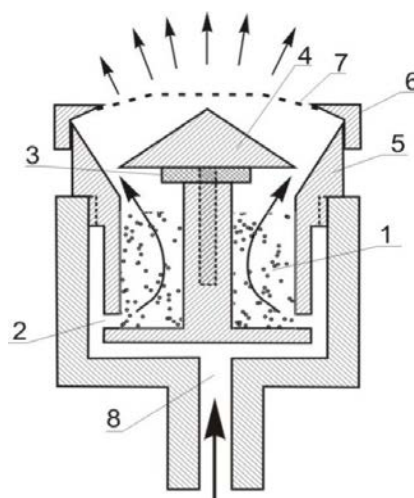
Конструкция распылителя: 1 – вихревая камера с порошком; 2 – тангенциальные отверстия; 3 – регулировочные шайбы; 4 – конус-нож; 5 – направляющий конус вихревой камеры; 6 – отбойная насадка; 7 – сетка.
